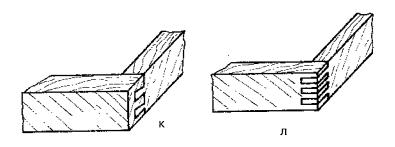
(продолжение)*. Двухэлементные угловые соединения на шипах: ж — соединение в ус вполупотемок; з — ус с круглым шипом; и — ящичный «ласточкин хвост»; к — ящичный шип вполупотемок; л — простой ящичный шип
